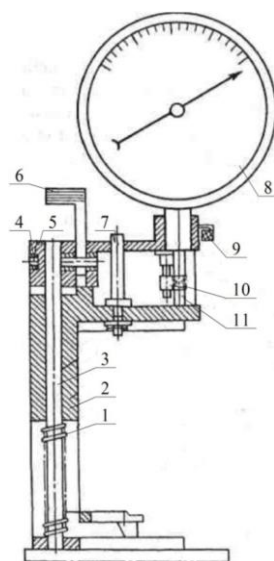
Приспособление для определения величины зазора КИ-9918
